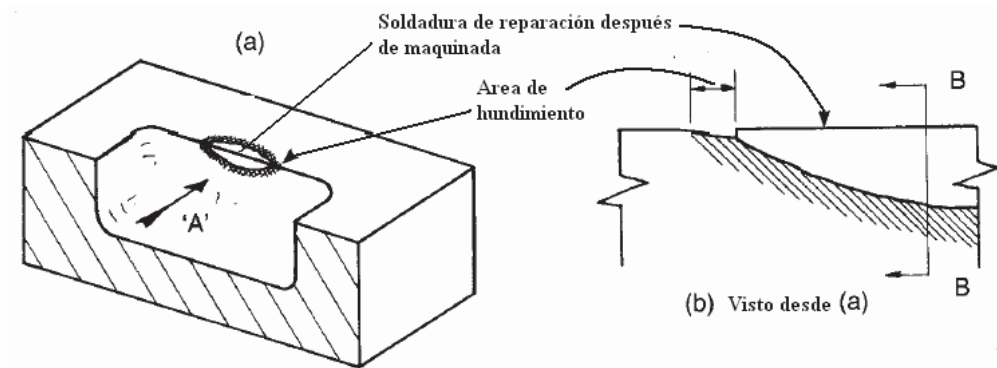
11 Forma del hundimiento: a) Soldadura de reparación después de maquinado y b) Vista Transversal (S. Horo. 1999).
